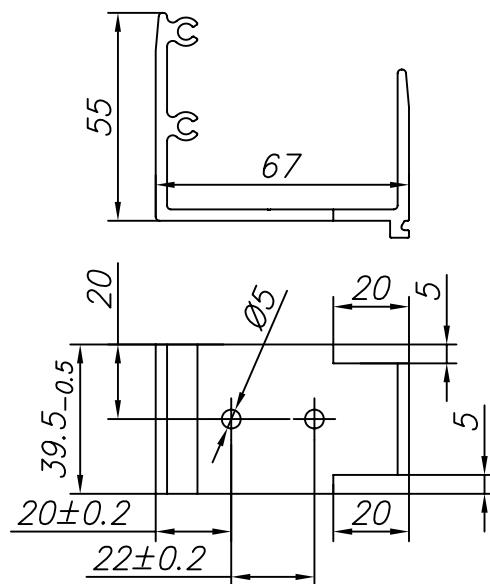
Изготовление соединителя FLGU 400.0912
